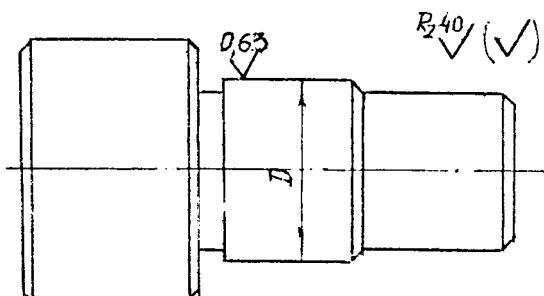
Вал ступенчатый. (Материал – группа стали М1 или М2; заготовка – штамповка на ГКМ)
